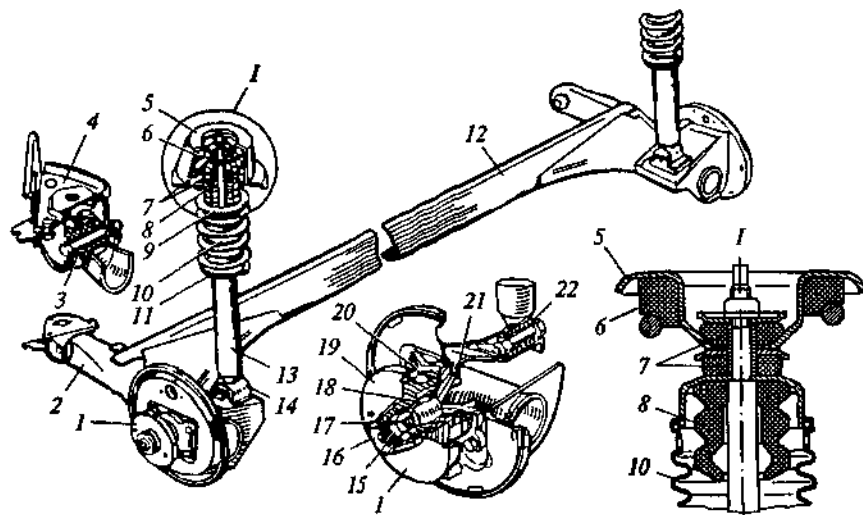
Задняя подвеска переднеприводного легкового автомобиля ВАЗ: 1 — ступица; 2 — рычаг; 3 и 22 — шарниры; 4 и 14 — кронштейны; 5 — опора; 6 — прокладка; 7 — подушки; 8 — буфер; 9 — пружина; 10 — кожух; 11 — опорная чашка; 12 — соединитель; 13 — амортизатор; 15 — ось; 16 — колпак; 17 — гайка; 18 — подшипник; 19 — шит; 20 — кольцо; 21 — фланец
